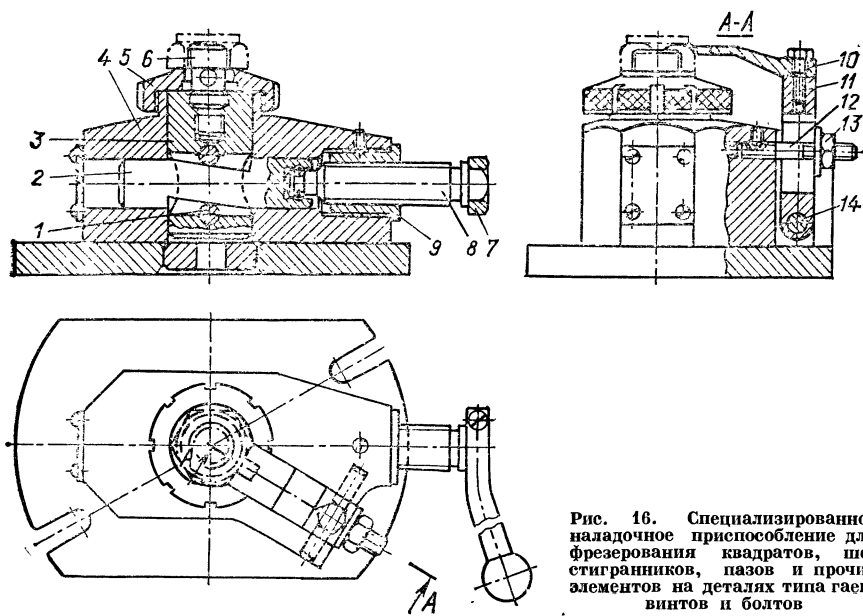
Специализированное надладочное приспособление для фрезерования квадратов, шестигранников, пазов и прочих элементов на деталях типа гаек, винтов и болтов
